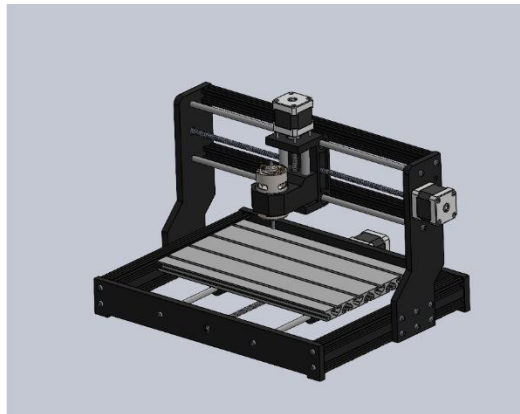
Ensamble de la CNC en SOLIDWORKS[45].
